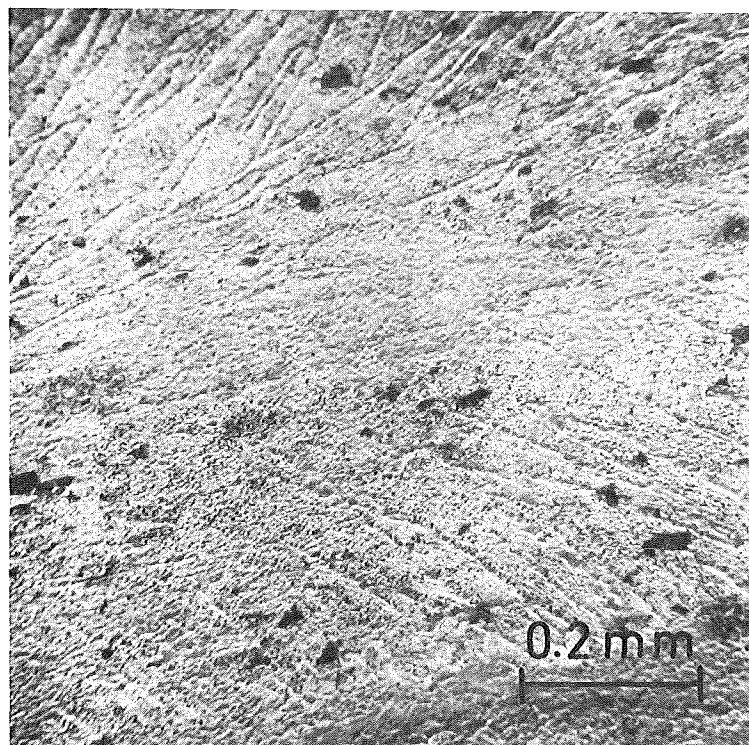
Endstopfenschweißnaht der Probe 1C14
